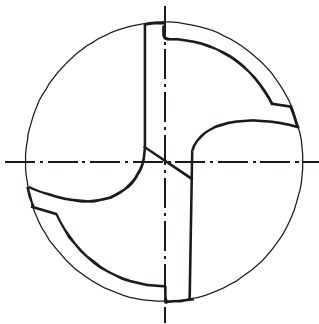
Вид спереди спирального сверла с четырьмя калибрующими ленточками
